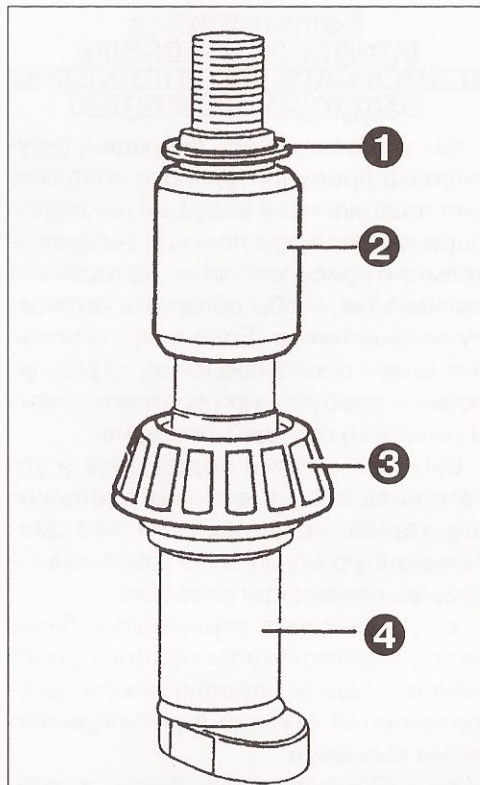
Вид в сборе вспомогательного приспособления.
